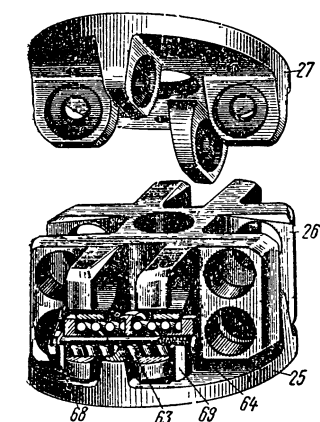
Детали муфты (обозначения см. на рис. 33)
